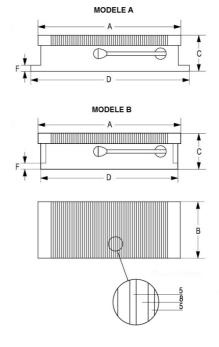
PLATEAU MAGNETIQUE DE FRAISAGE - FERRO-MILL
